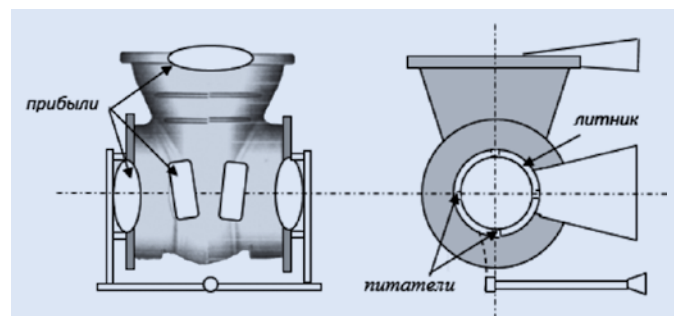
Схема технологии литья корпуса задвижки из стали 30ХГСЛ, $D_y = 50 \text{ см}$
